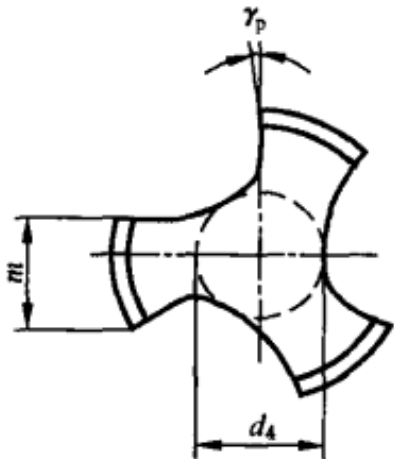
螺旋槽机用丝锥的结构要素和切削角
